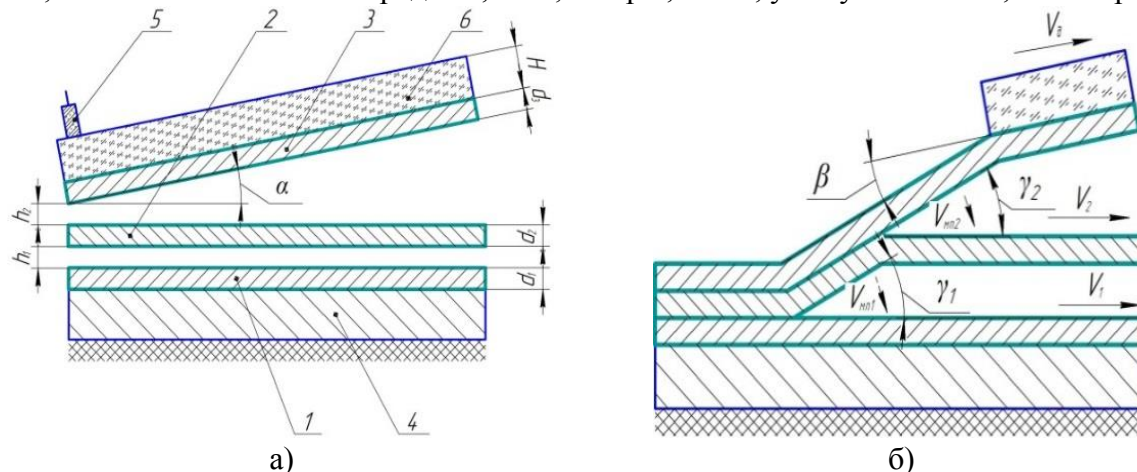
Угловая схема сварки взрывом:
